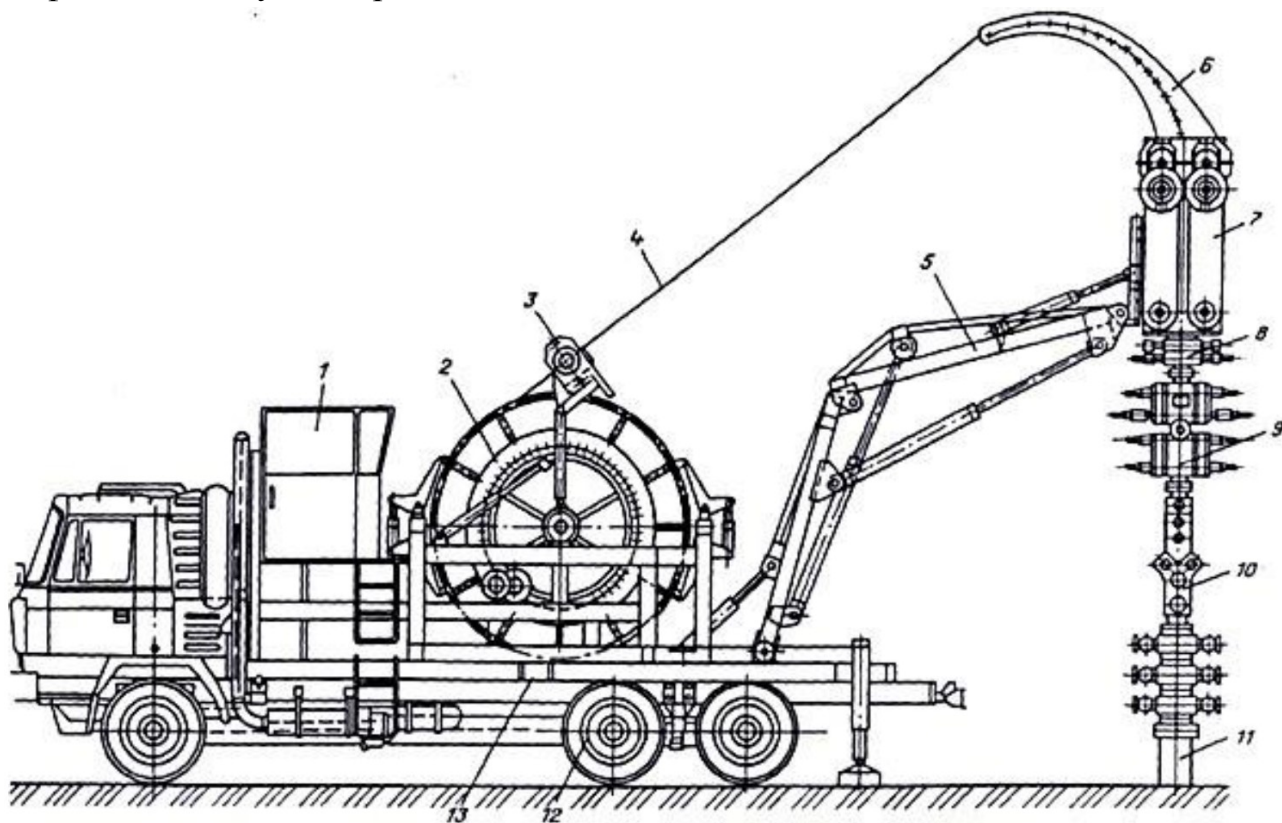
Компоновка колтюбінгової установки в робочому положенні [9]
